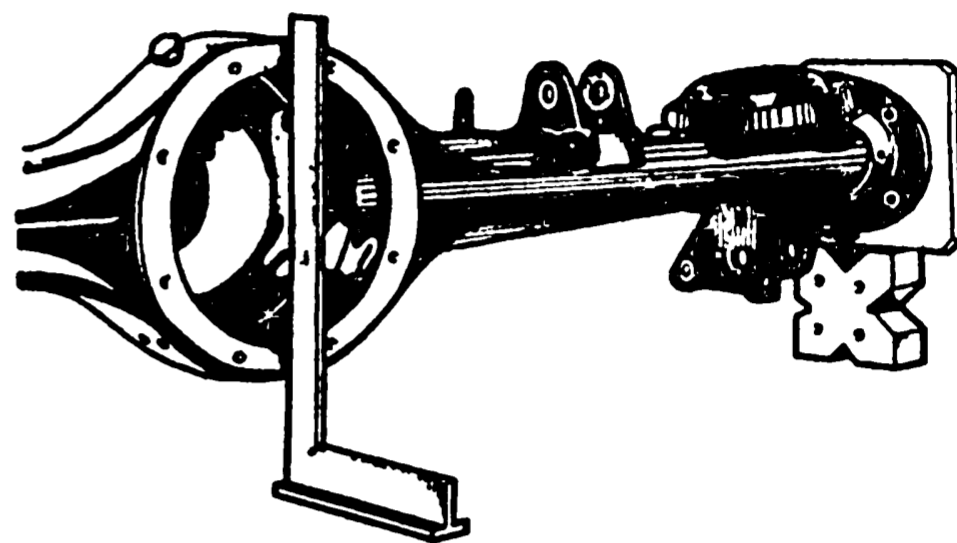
Проверка перпендикулярности поверхности крепления редуктора
